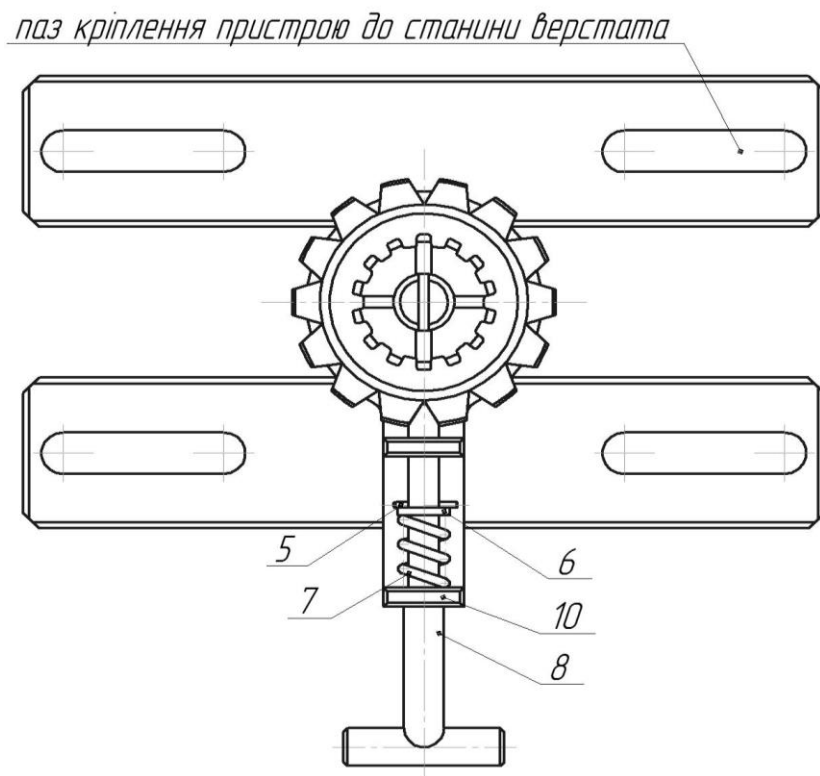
Пристрій для фіксування веденого диска при висвердлюванні заклепок (вид з боку керування)
